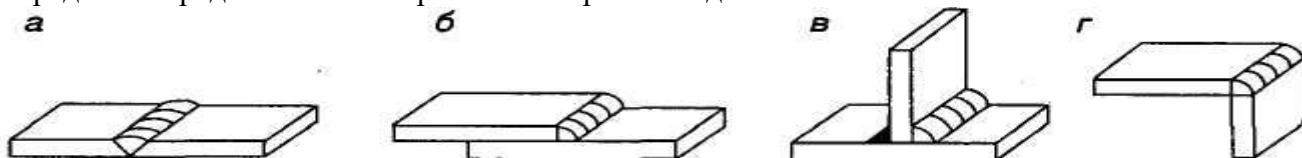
Типы сварных соединений: а — стыковое; б — нахлесточное; в — тавровое; г — угловое
